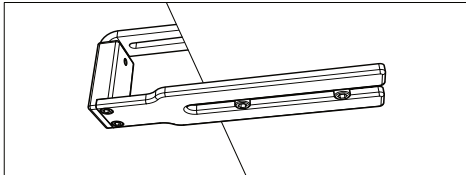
Abbildung A: Die beiden Schrauben sind Führungen für die Stütze.
